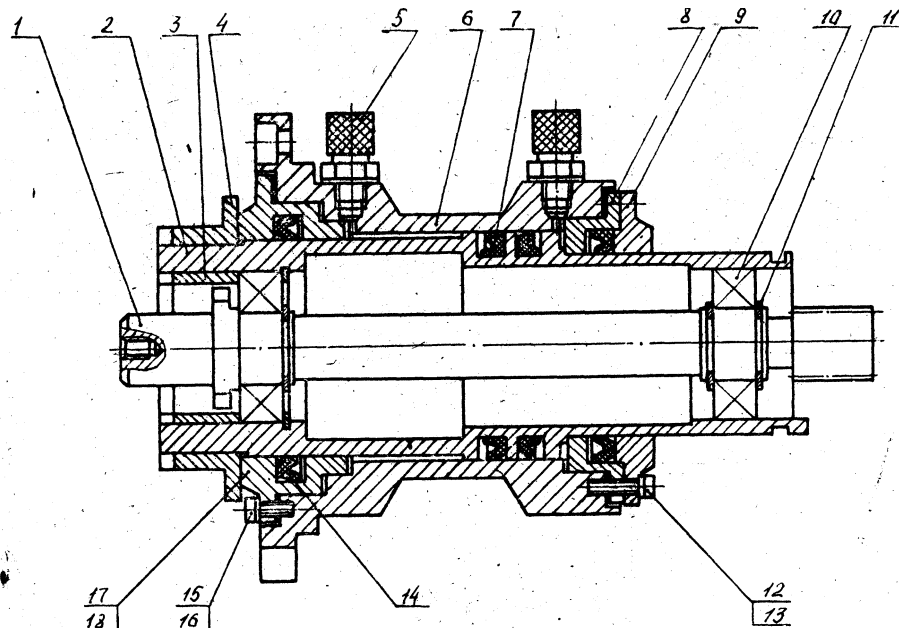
Механізм підйому: 1 – вал; 2 – шток; 3 – втулка; 4 – кронштейн; 5 – з'єднання пряме кінцеве; 6 – корпус; 7 – манжета; 8 – кришка; 9 – кришка; 10 – підшипник; 11 – кільце пружинне; 12 – гвинт; 13 – шайба пружинна; 14 – манжета; 15 – гвинт; 16 – шайба пружинна; 17 – кришка; 18 – прокладка
